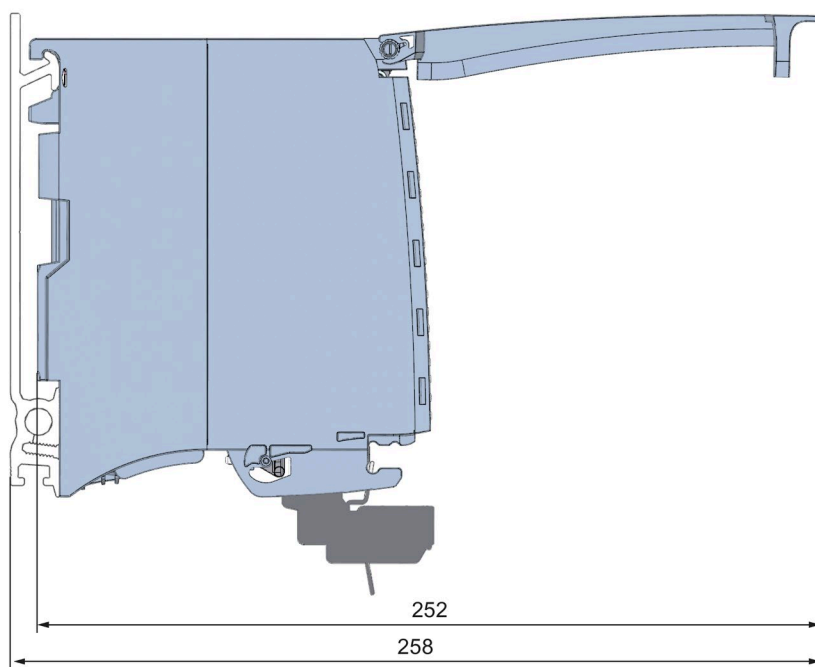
Maßbild des Moduls TM FAST in Seitenansicht mit geöffneter Frontklappe
